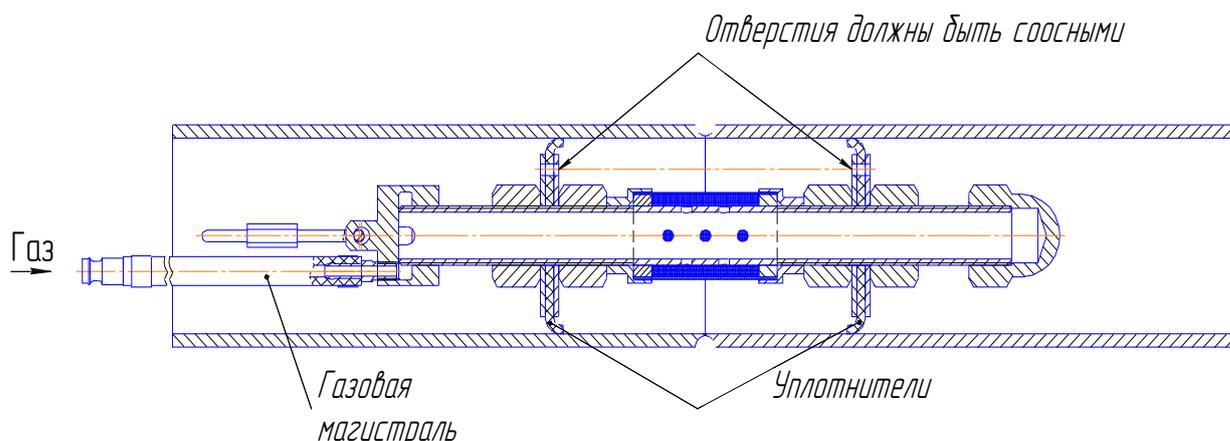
Схема установки устройства при сварке труб
